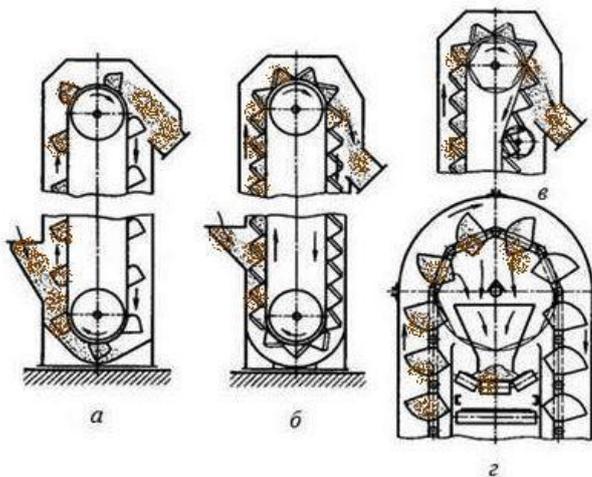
Схемы загрузки и разгрузки ковшовых элеваторов:
